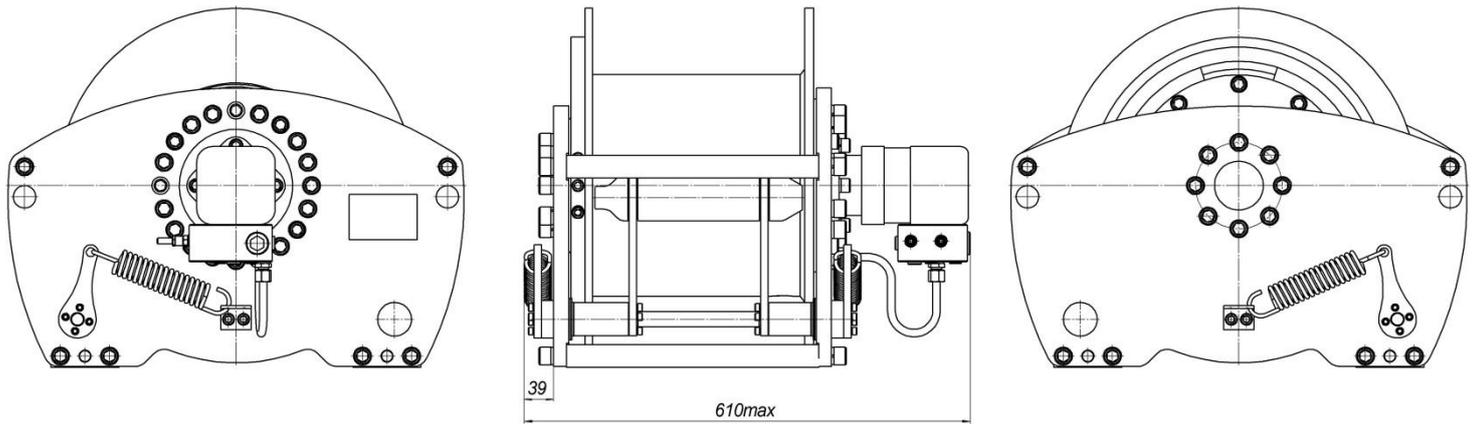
Общий вид, габаритные и присоединительные размеры
